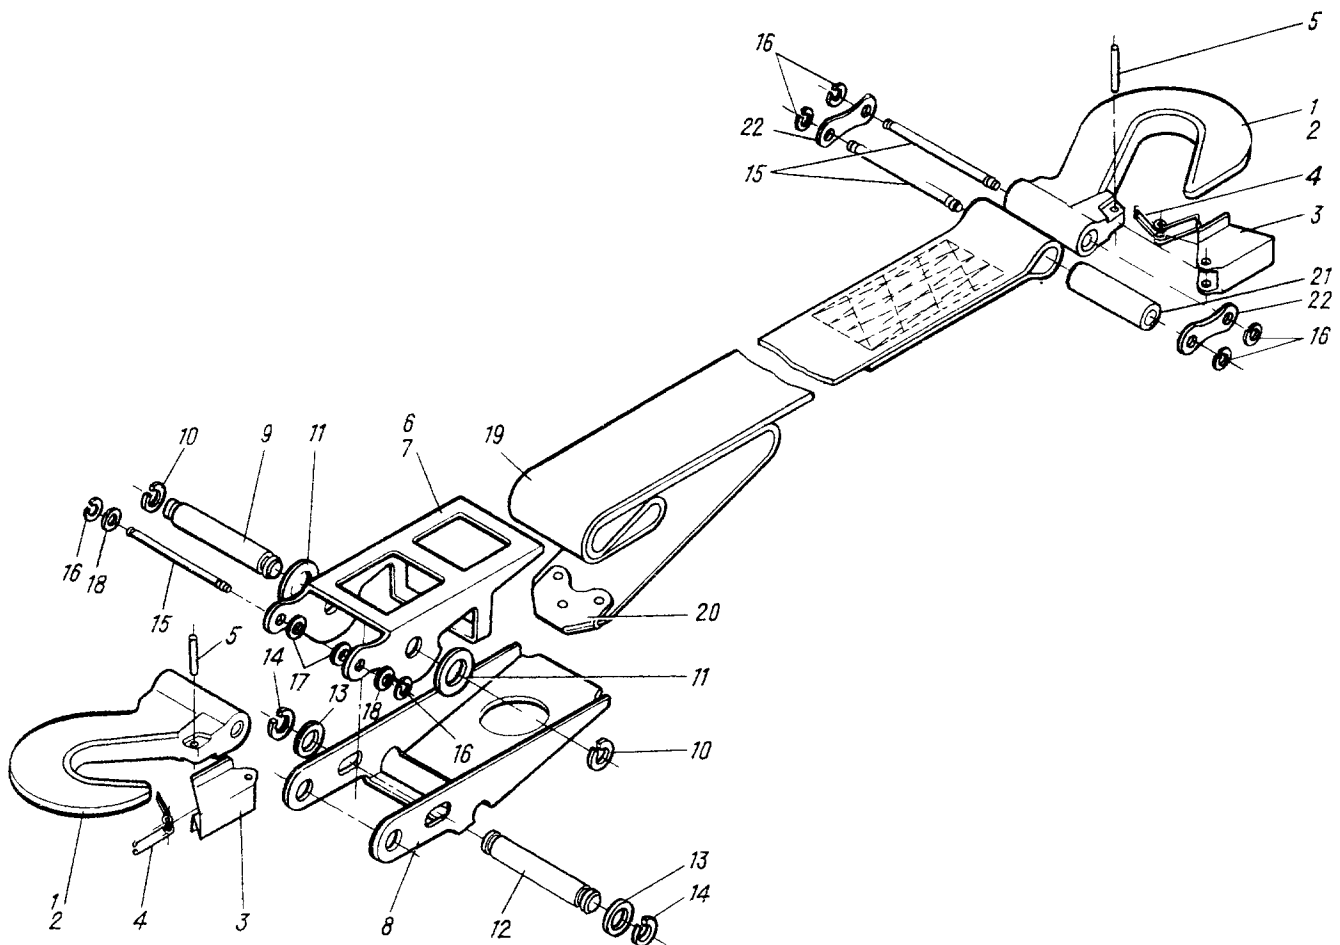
РЕМЕНЬ ШВАРТОВНЫЙ
